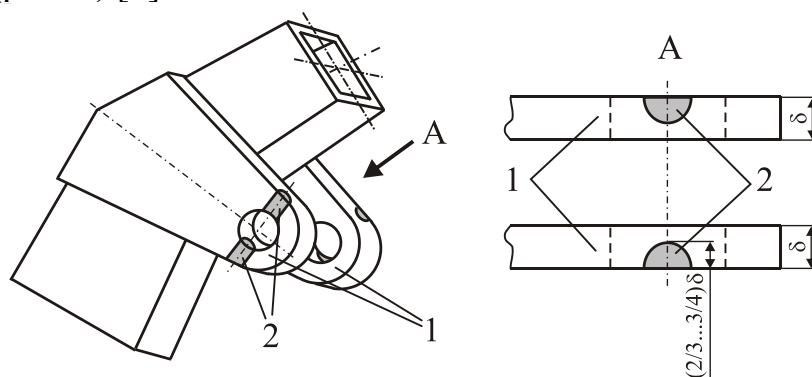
Схема упрочнения: 1 – проушины; 2 – наплавленный материал
